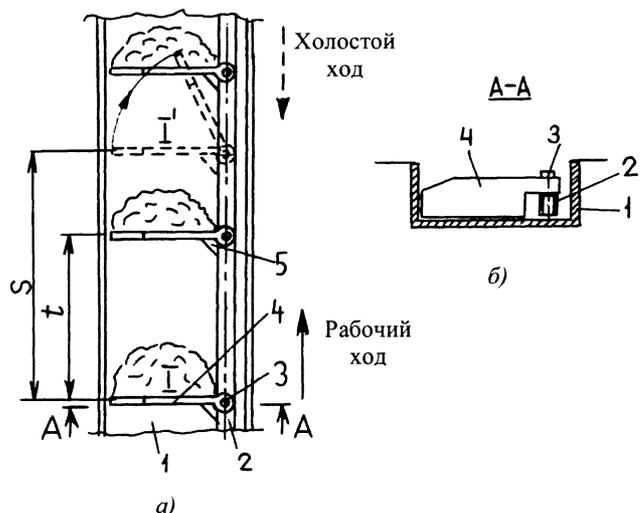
Фрагмент штангового скребкового конвейера с вертикальной осью крепления скребков:
